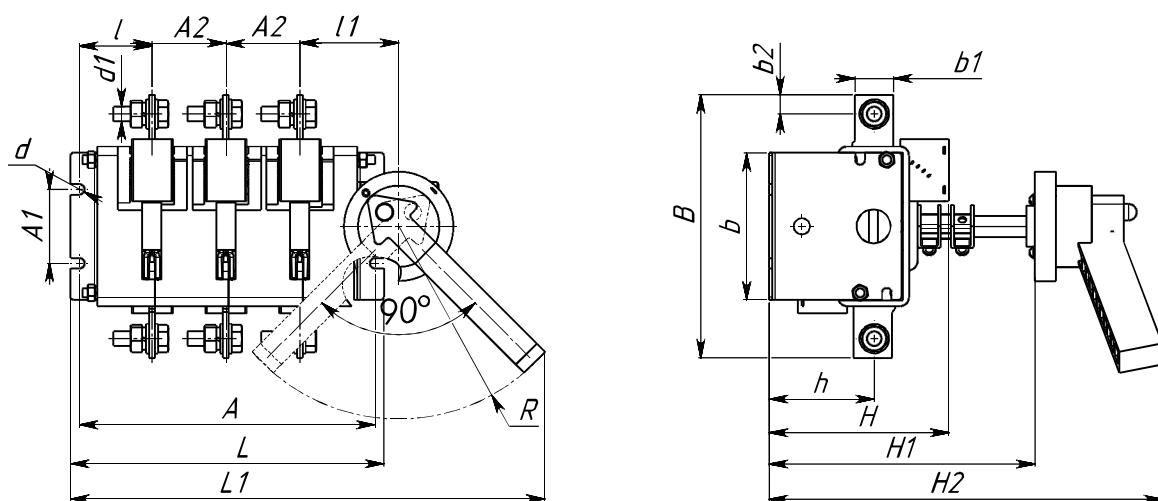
Выключатель-разъединитель на одно направление трехполюсный с передней поворотной рукояткой
